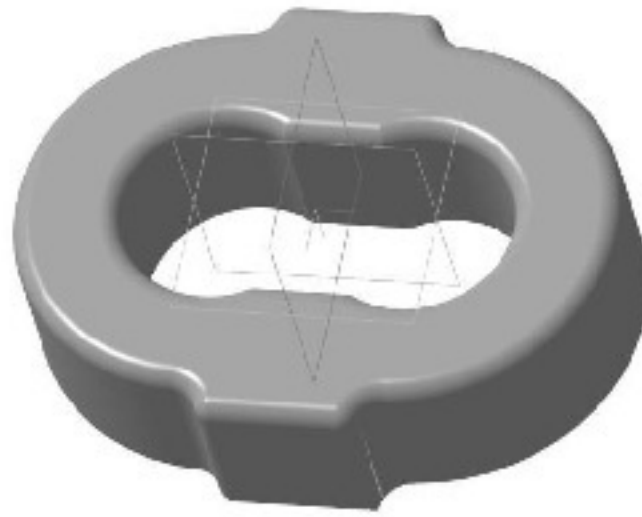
3D-модель заготовки при литті в облицьований кокіль
